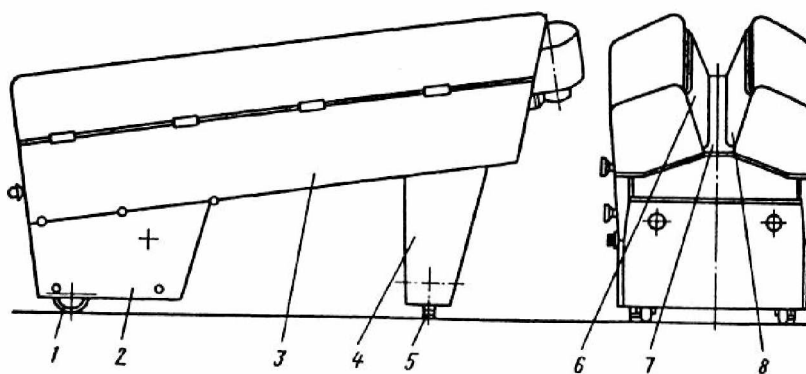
Стрічкова тістоокруглювальна машина: 1 – ролики; 2, 4 – тумби; 3 – станина; 5 – штифти; 6, 8 – транспортери; 7 – нерухома поверхня.
